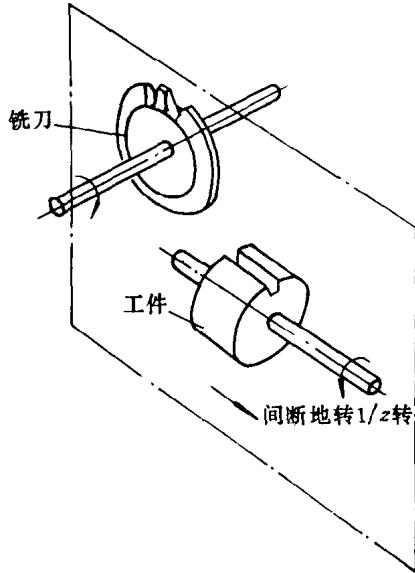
用盘形齿轮铣刀仿形加工齿轮
